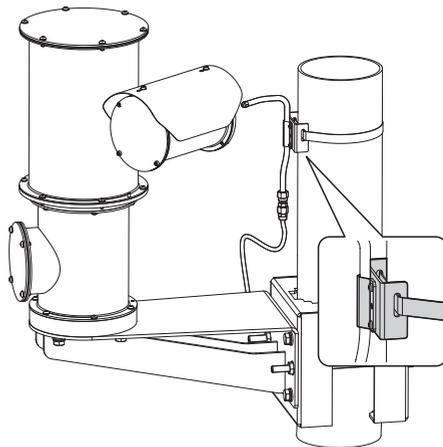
Exemple d'installation du lave-vitre à poteau.
